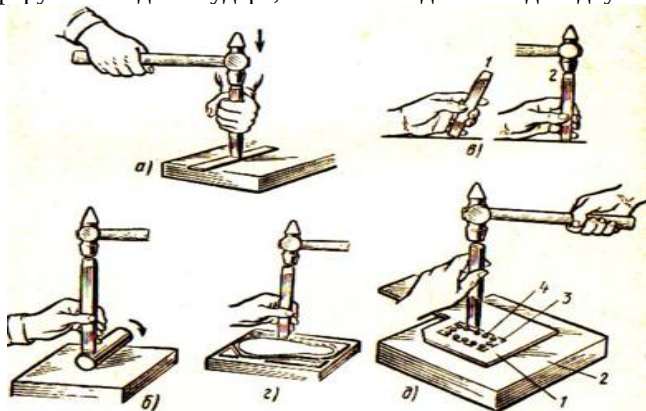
Рубка металла: а -полосы;б-рубка круглого проката; в- подготовка к рубке;г-рубка по контуру; д-вырубаение фигурной заготовки из листовой стали
